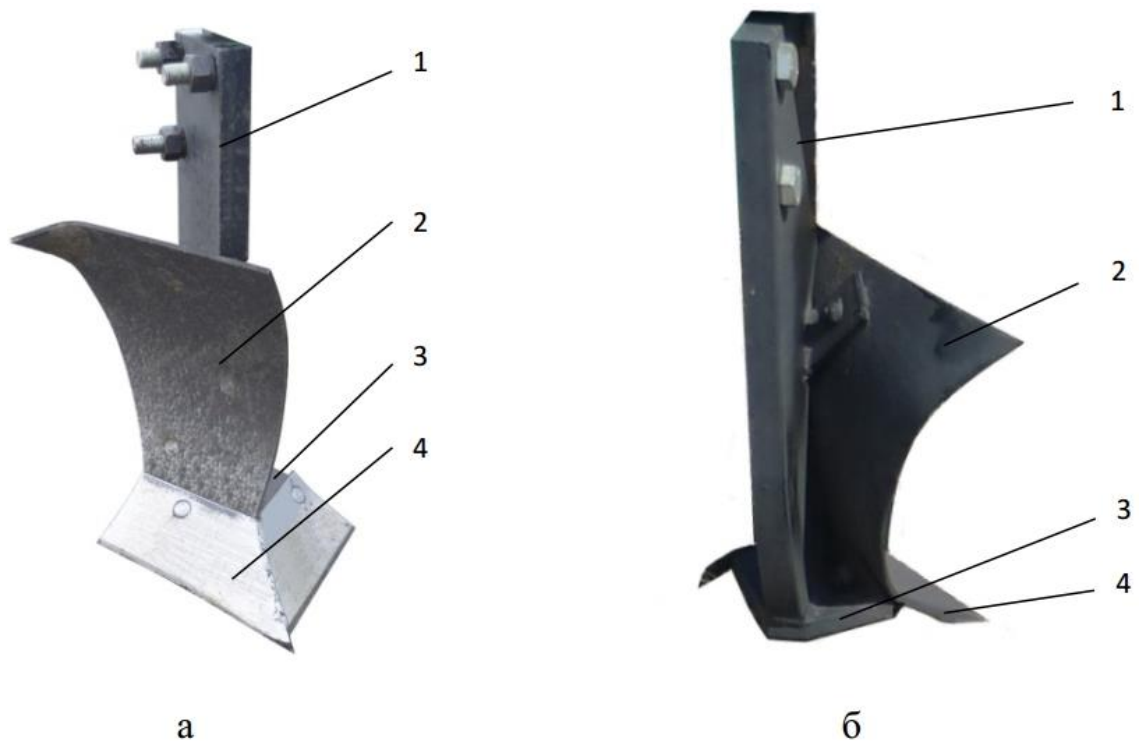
Модернизированный корпус плуга ПБС: а- вид спереди; б- вид сзади
